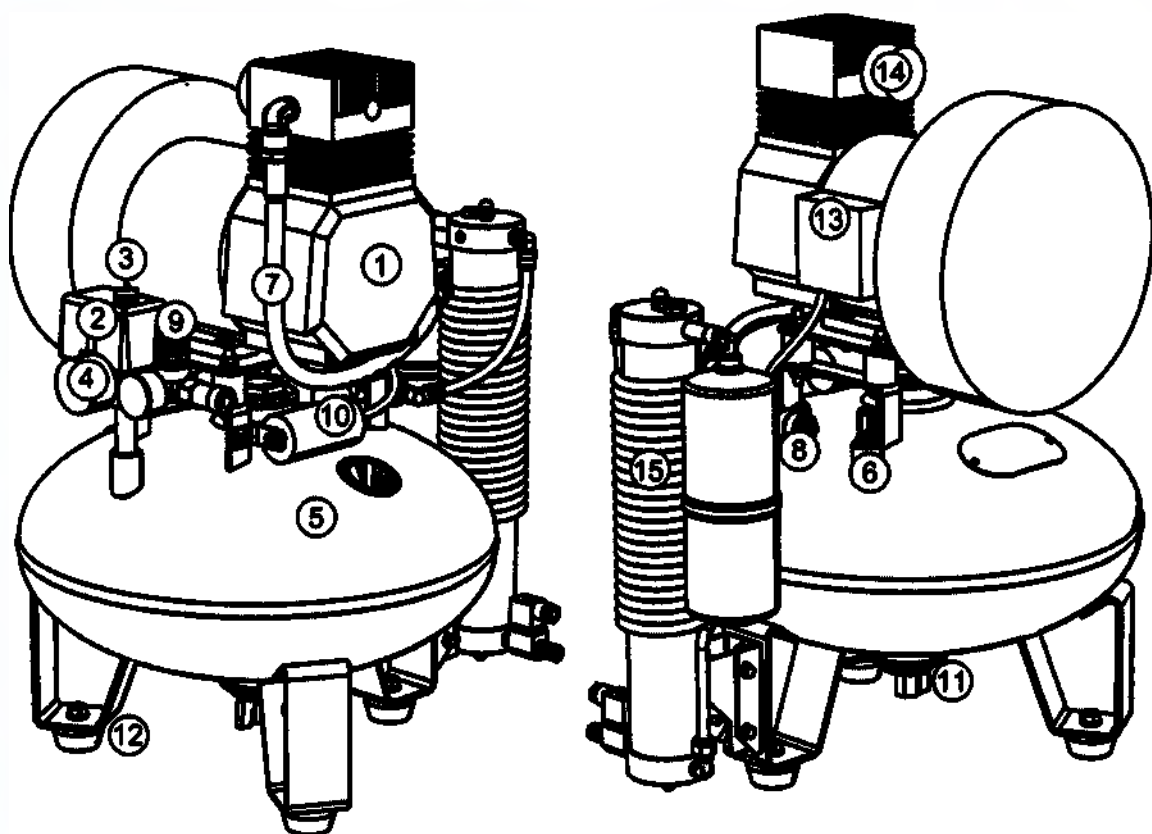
Общий вид компрессора KM-24.GMS150Д
